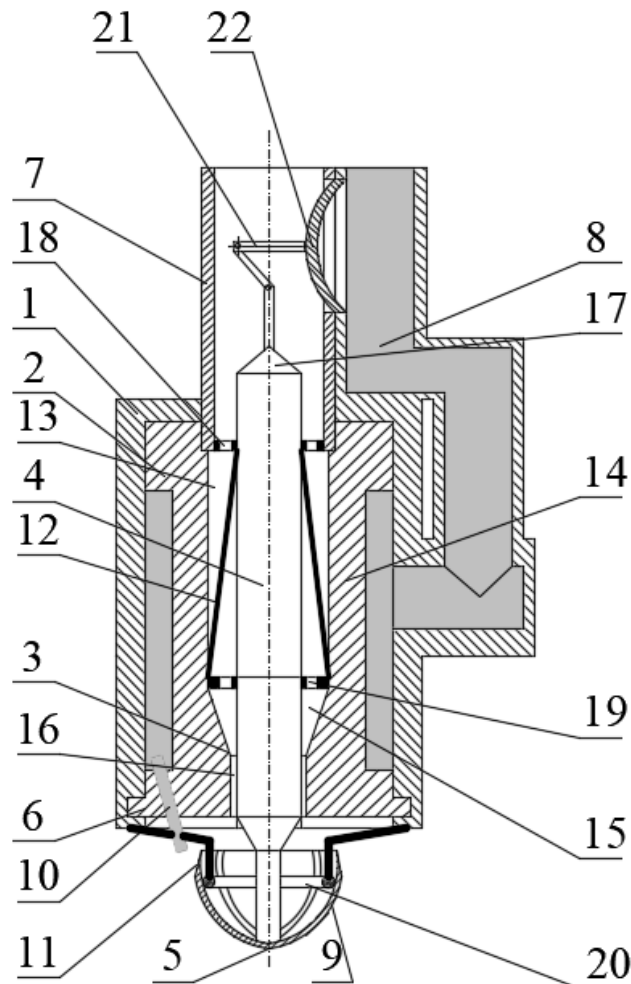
Акустична форсунка: 1 – корпус; 2 – верхній фланець; 3 – сопло; 4 – стрижень; 5 – об'ємний резонатор; 6 – приймач випромінювання; 7 – трубка для підведення повітря; 8 – трубка для підведення рідини; 9 – пелюсткова мембрана; 10 – сопло; 11 – робоча поверхня пелюсткової мембрани; 12 – розсікач повітря; 13 – отвір; 14 – втулка; 15 – конфузор; 16 – циліндричний отвір; 17 – обтічник; 18, 19 – перфоровані диски; 20 – опорне кільце зі стойками; 21 – важелі; 22 – силова мембрана
